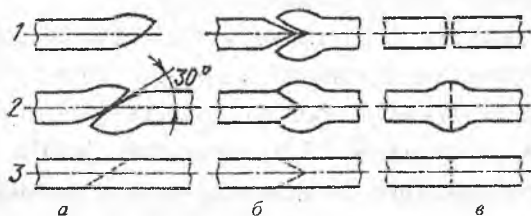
Схемы кузнечной сварки: а - внахлестку, б - вразруб, в - встык
